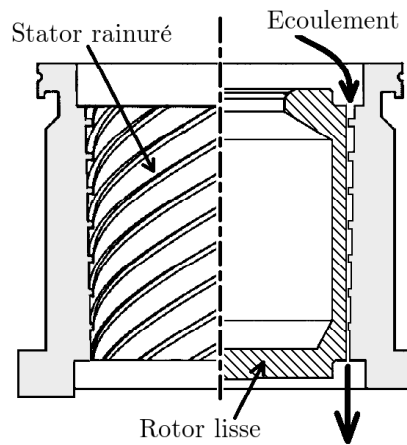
Coupe d'une pompe Holweck à rotor lisse
